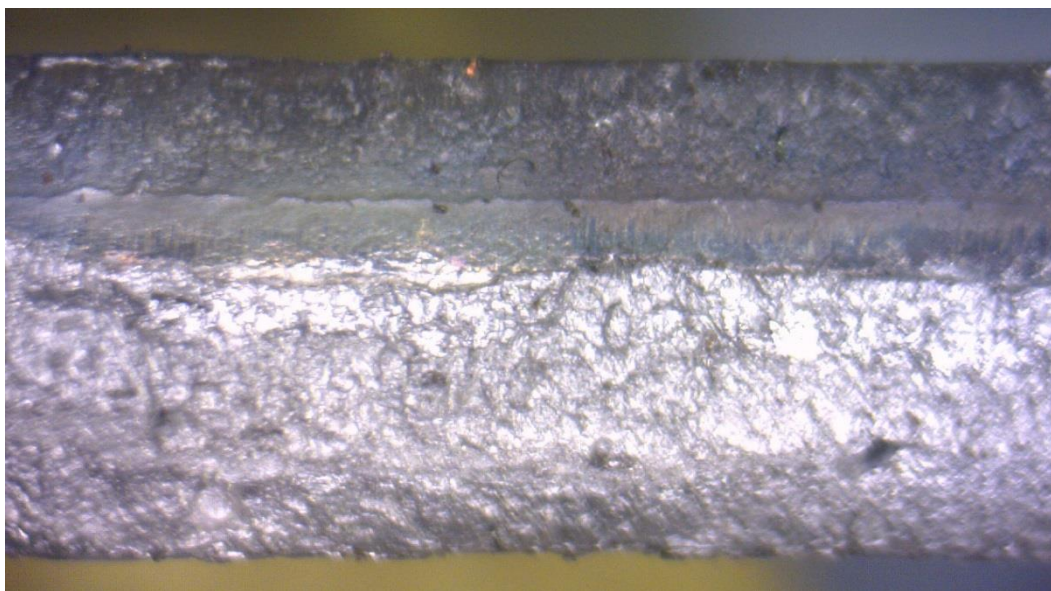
Vzorky TIG-TIG pro zkoušku rozlomením
